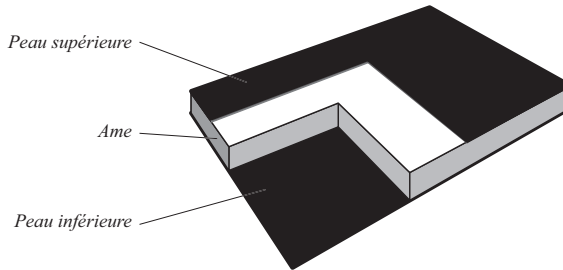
Schéma d'une plaque en construction de type sandwich.
